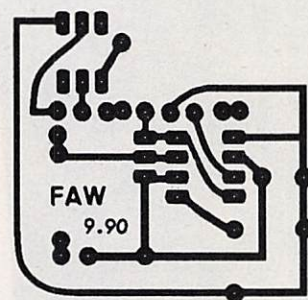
Le CI, côté soudures, du module d'adaptation.
